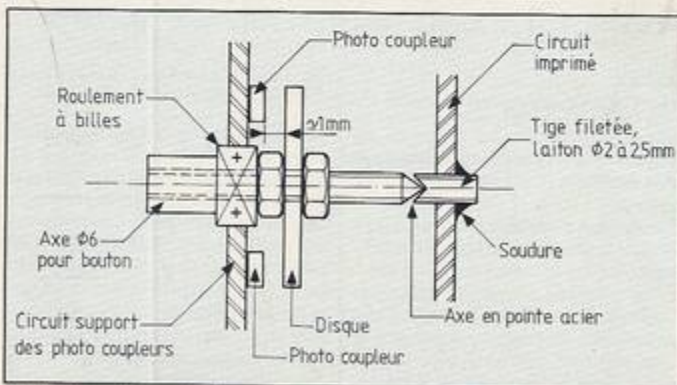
Disposition mécanique des éléments, vue en coupe.
